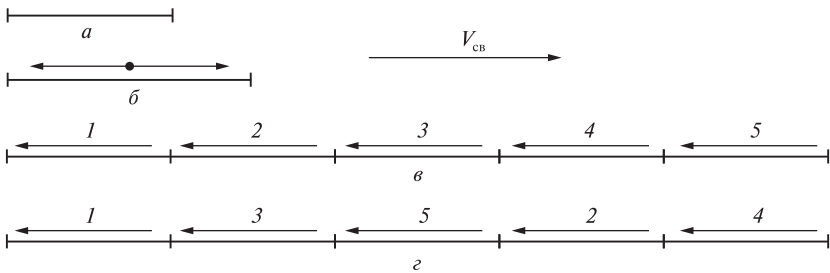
Схемы выполнения сварных швов:
